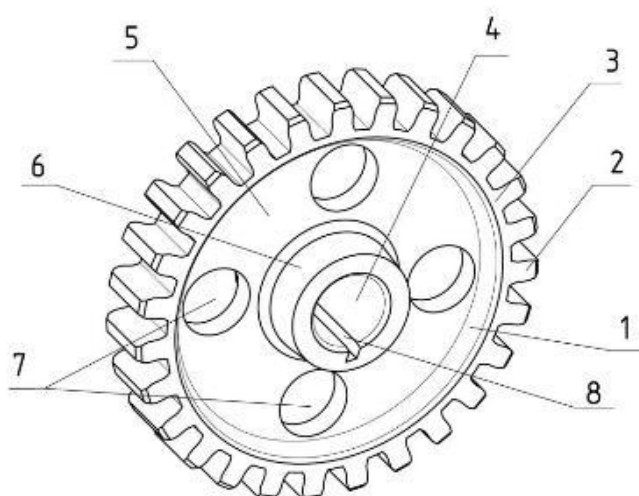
Строение зубчатого цилиндрического штампованного колеса: 1 – обод; 2 – зуб; 3 – венец; 4 – посадочное отверстие; 5 – диск; 6 – ступица; 7 – отверстие в диске; 8 – шпоночный паз
